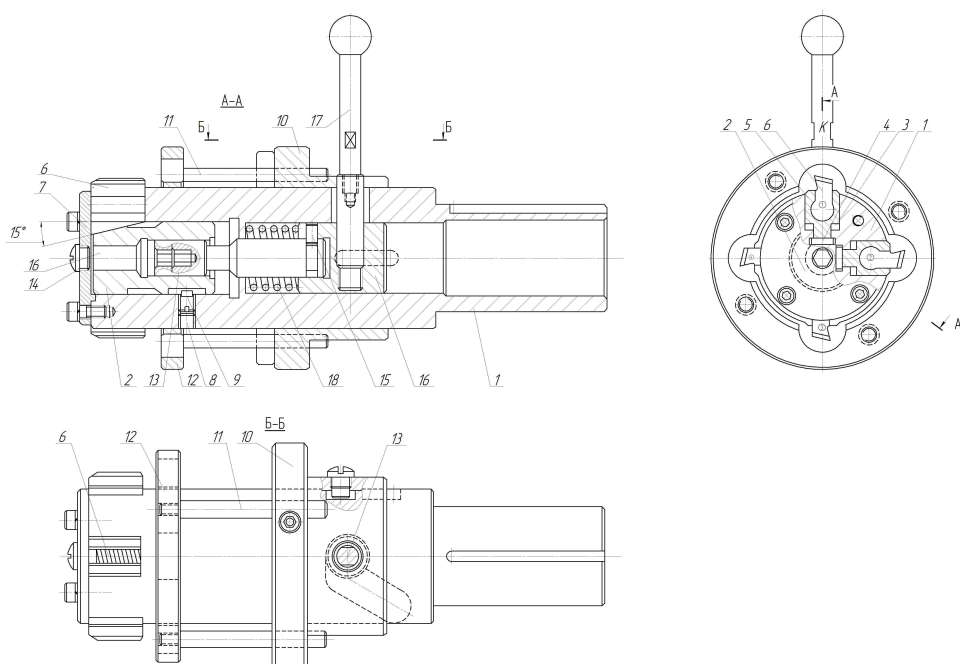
Головка для нарізання внутрішніх різьб [11]
